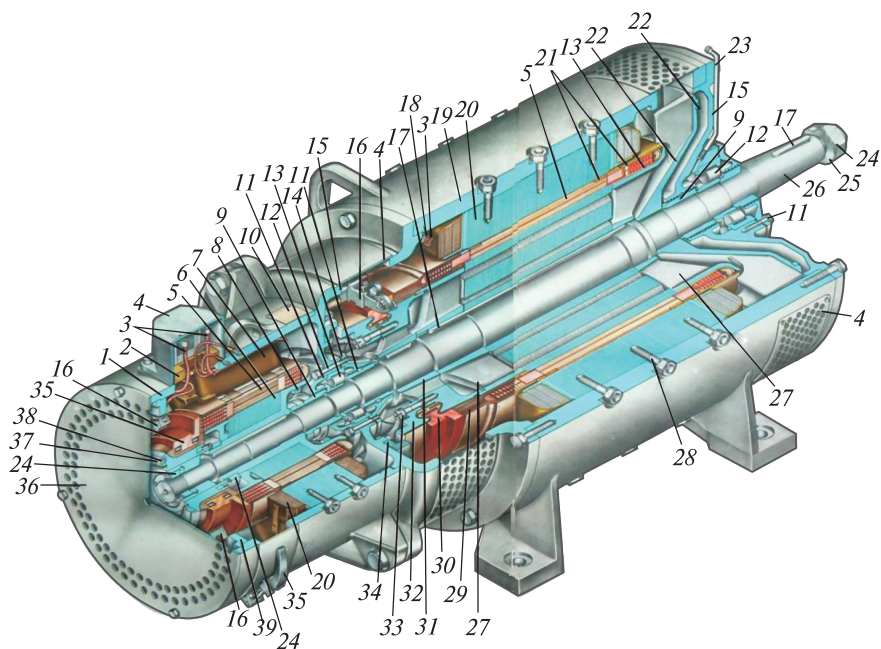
Общий вид двигателя ТЛ-110М и генератора управления НБ-110:
